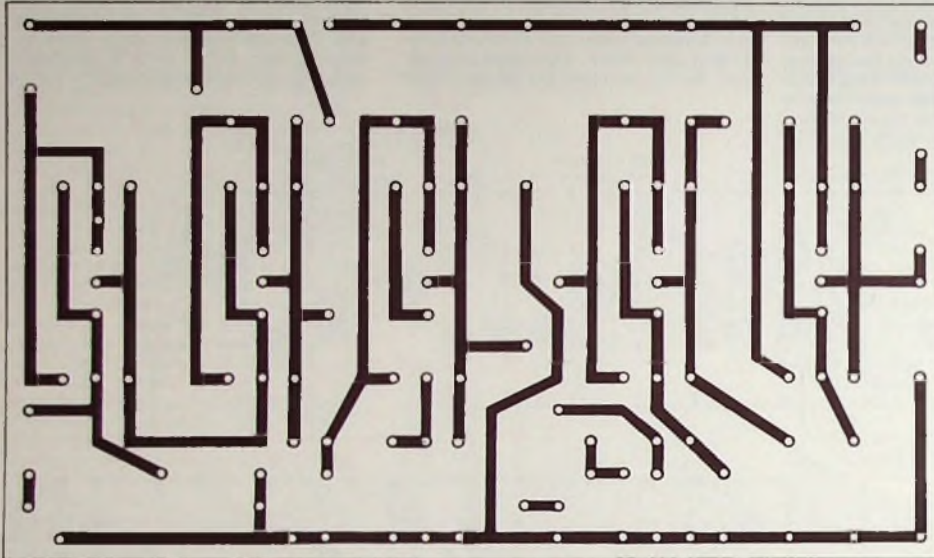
Printplatte für den Transistorprüfer (Maßstab 1:1)
